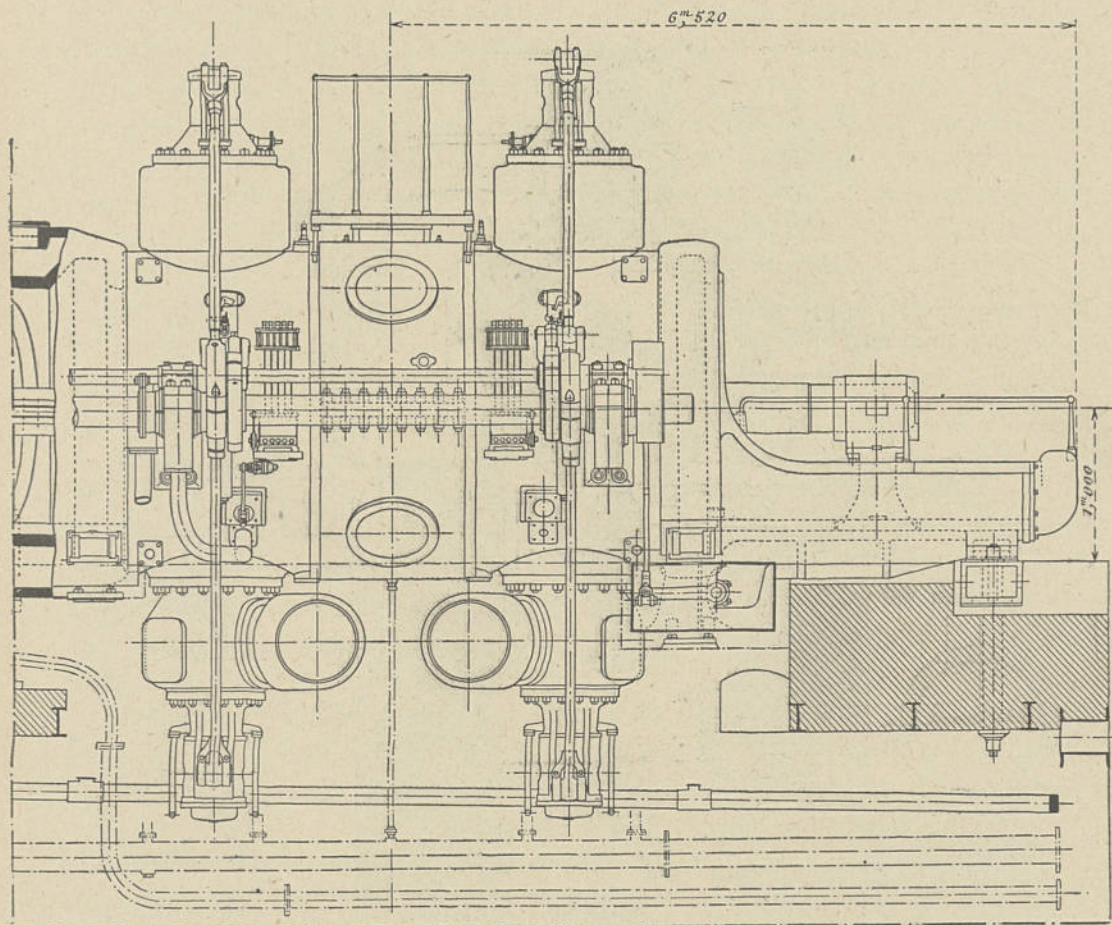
Vue latérale du moteur de la Société Alsacienne.
